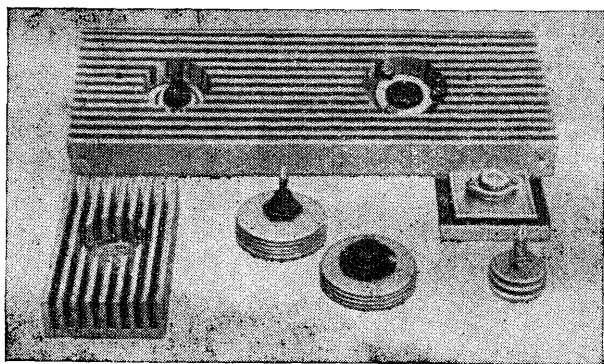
Радиаторы, изготовленные на фрезерном и токарном станках.
